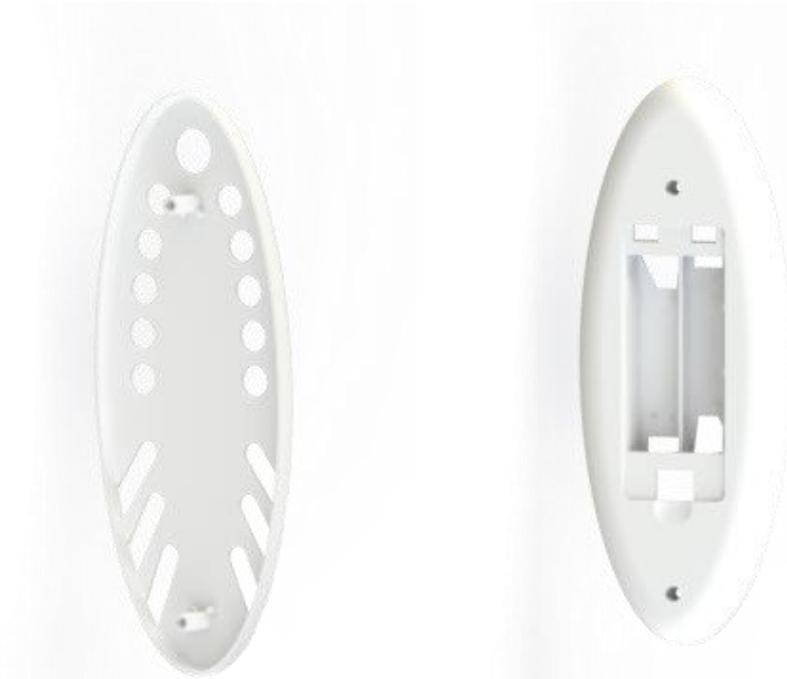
Carcasa sup. (izq.) y Carcasa inf. (dcha.)
